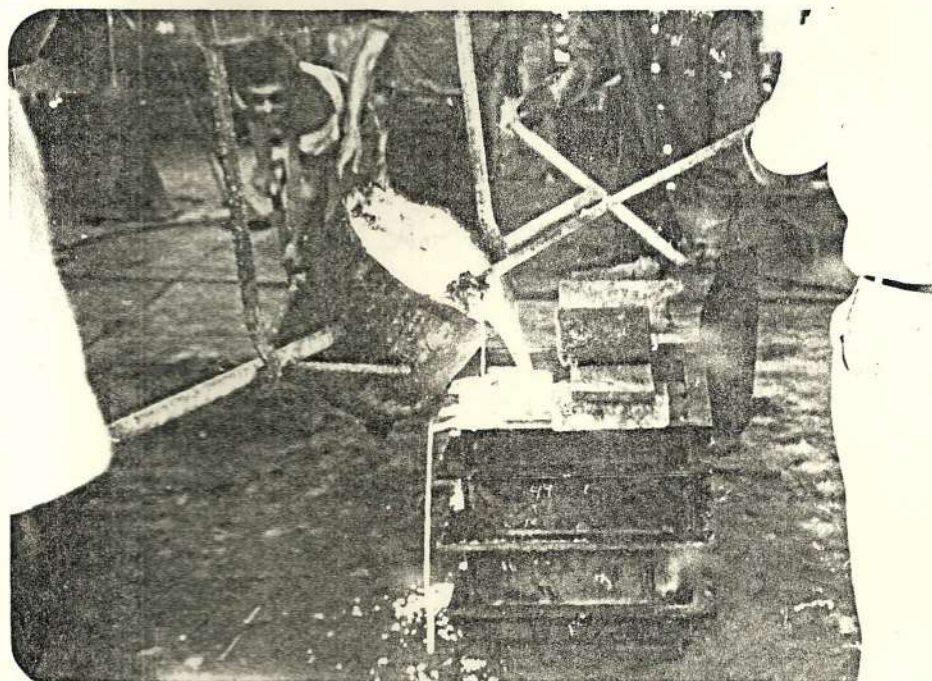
COLADO DEL METAL EN LOS MOLDES
